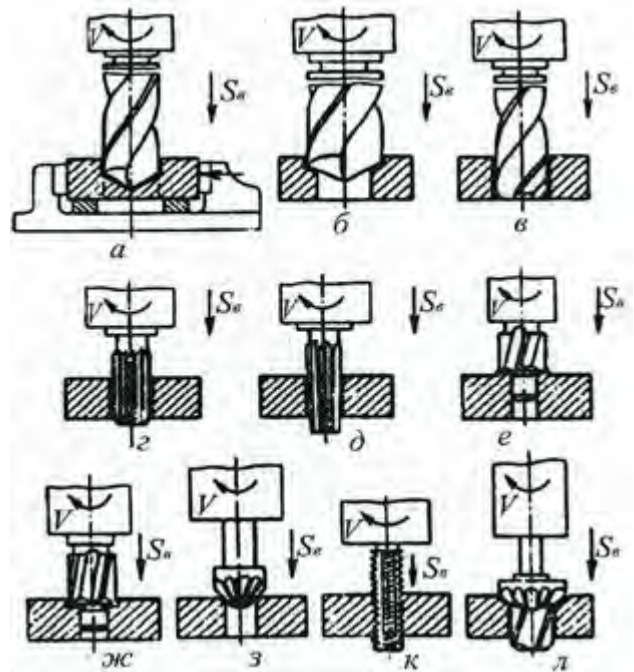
Схеми оброблення заготовок на свердильних верстатах
